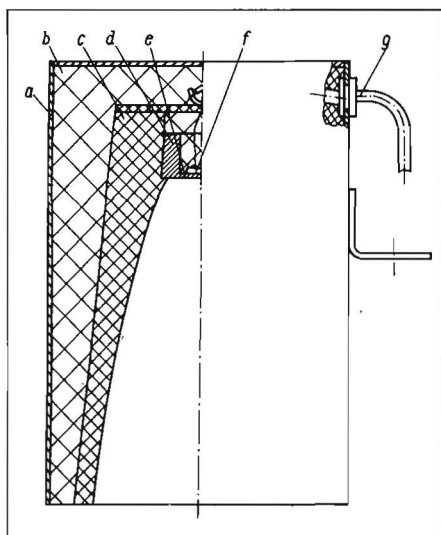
Aufbau des Ultraschall-Meßkopfes; a Blechmantel, b Weichschaum, c PUR-Hartschaum, d Ultraschall-Wandler-Stützkörper, e Plattenschwinger, f Erreger (Piezo-Platte), g Anschluß Koaxialkabel
